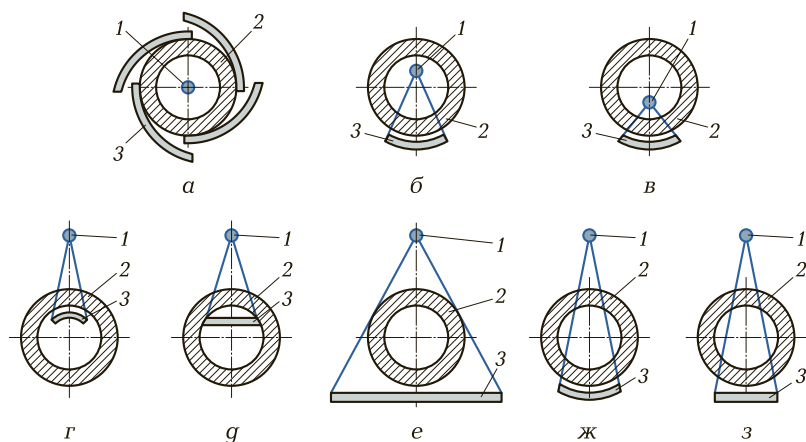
Схемы (*а...з*) радиографического контроля сварных соединений цилиндрических и сферических полых узлов:
